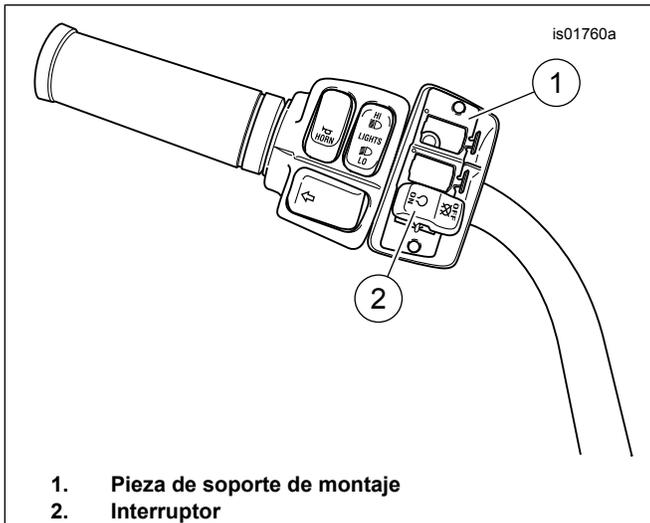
Pieza de soporte de montaje de accesorios auxiliares
